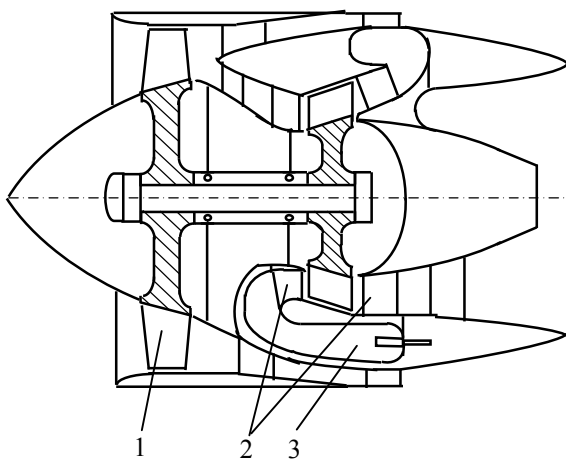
Схема газотурбинного двигателя с ТКО: 1 – вентилятор; 2 – турбокомпрессор (ТКО); 3 – камера сгорания
